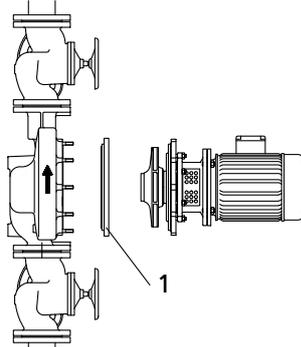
Montaggio orizzontale con flangia cieca (1 = flangia cieca, accessorio)
